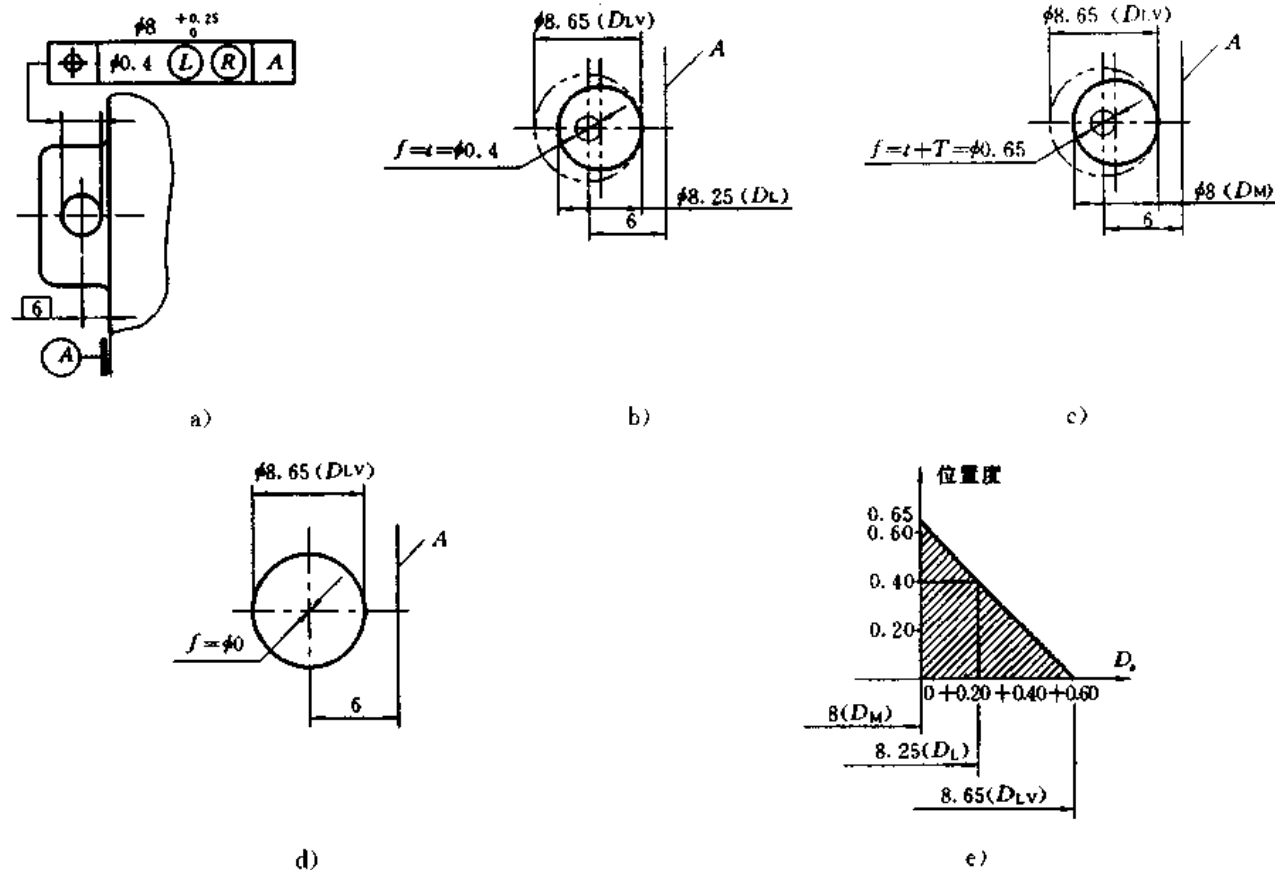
轴线位置度公差采用可逆的最小实体要求
